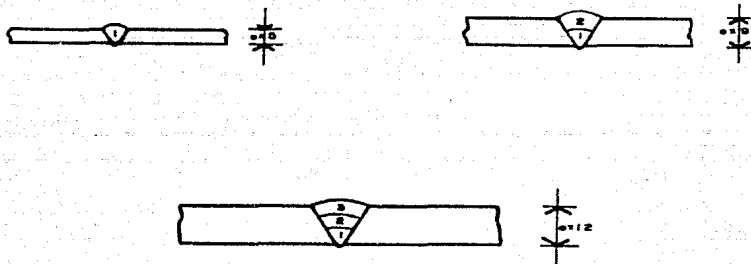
Disposición de los cordones de soldadura en el método por pasadas anchas.
